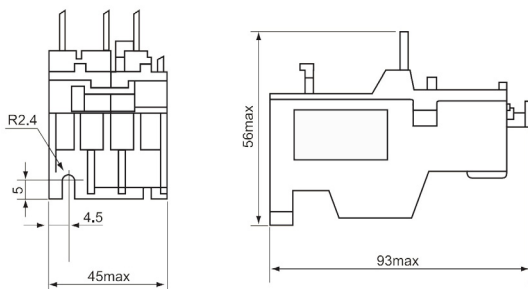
Габаритные размеры реле РТЛ 1001÷1022
